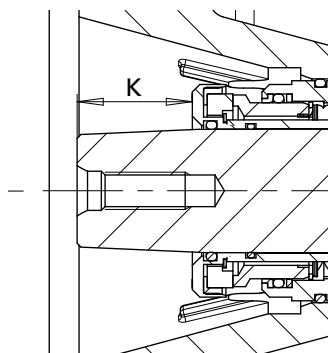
Контрольный размер «К» от конца вала до сдвоенного картриджного торцового уплотнения
